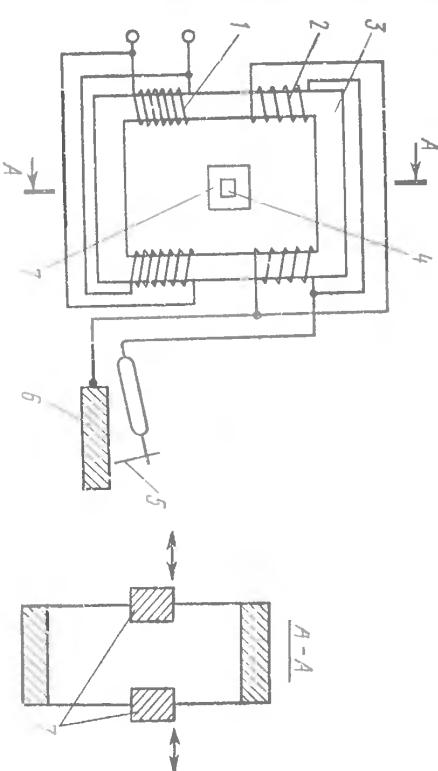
Электрическая схема сварочного трансформатора типа СТШ:
